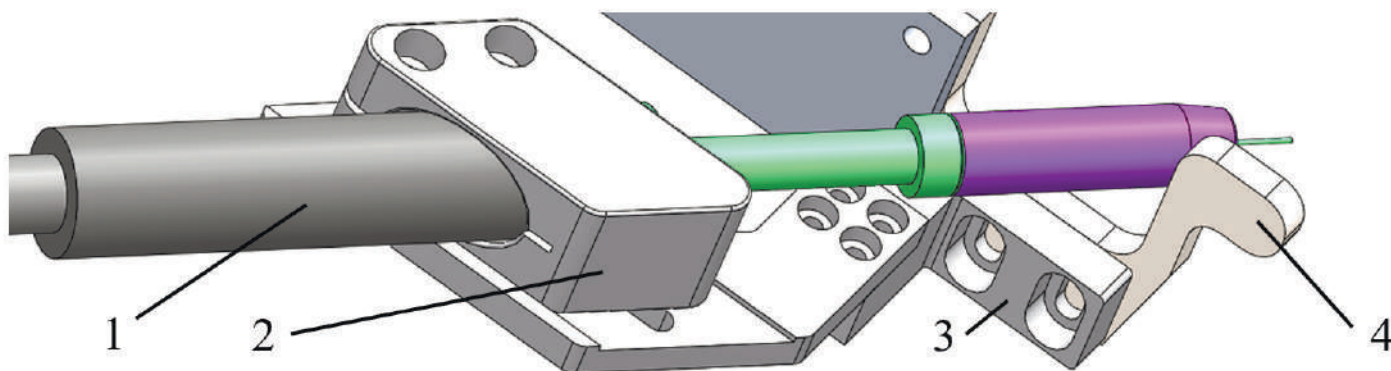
Механизм фиксации и регулировки сварочной горелки:
